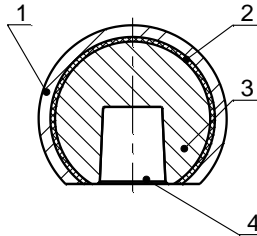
Головка протезу кульшового суглобу багатшарової конструкції:
